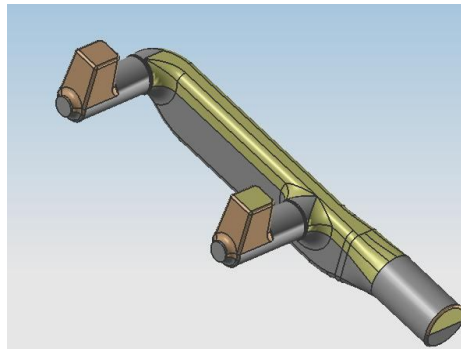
Стержень для отливки «Коллектор» 245-1003033Д
